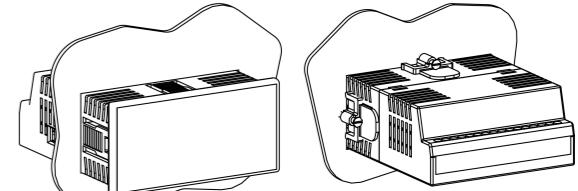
Монтаж прибора щитового крепления Щ2
